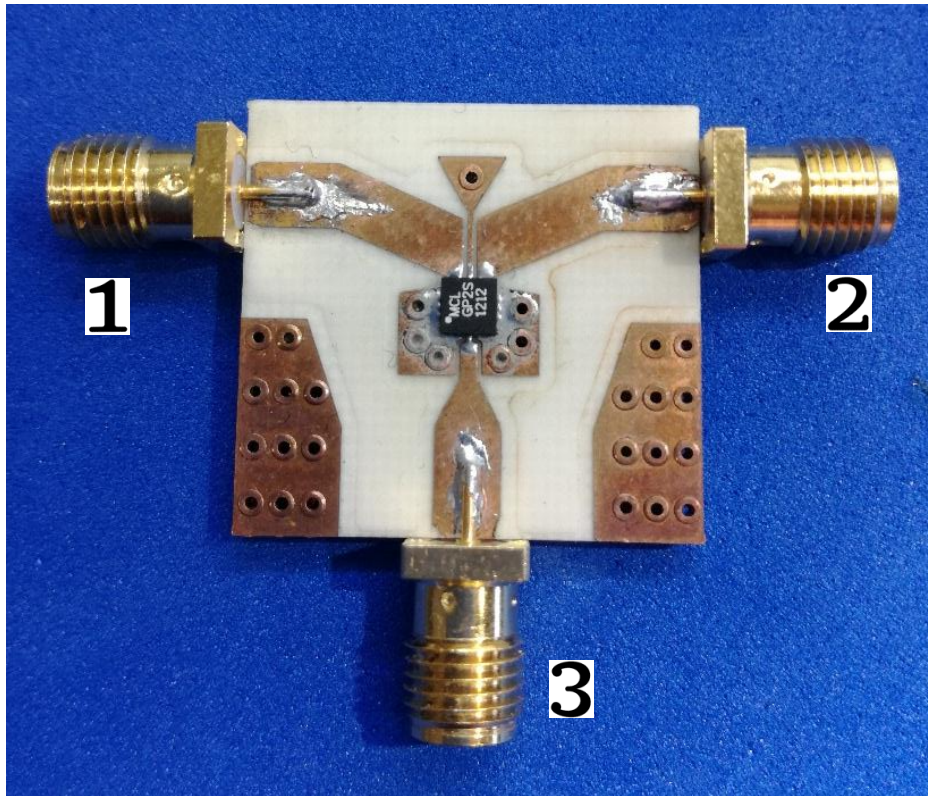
PCB fabricada a partir del diseño propuesto para el DAT-15R5A-SP+.
